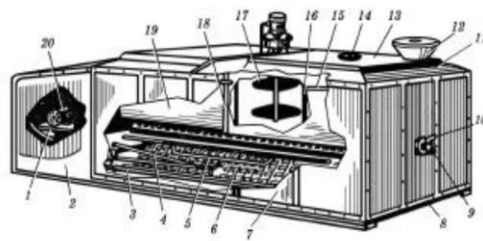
Резервуар-охолоджувач молока: 1 - охолоджувальний агрегат; 2 - кожух охолоджувального агрегату; 3 - всмоктувальна труба водяного насоса; 4 - розподільний колектор фреону; 5 - колектор-збірник пари фреону; 6 - панельні випарники; 7 - корпус резервуара; 8 - зливний отвір акумулятора холоду; 9 - контрольний отвір рівня води; 10 - молочний кран; 11 - отвір для зливання води; 12 - молокоприймач із фільтром; 13 - кришка; 14 - люк; 15 - трубка водного зрошування; 16 - мірна лінійка; 17 - мішалки; 18 - термодатчик; 19 - молочна ванна; 20 - вентилятор.
